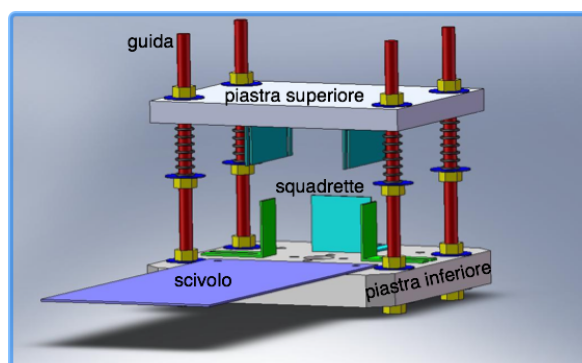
Disegno del dispositivo di sospensione e movimentazione degli stampi.
